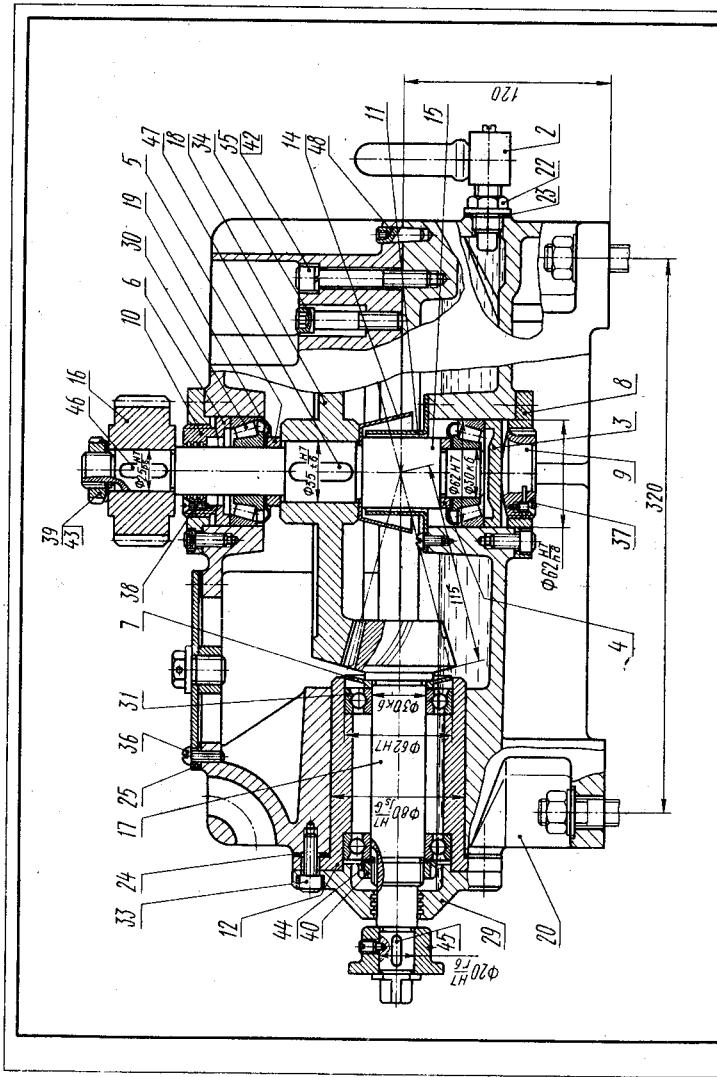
Пример сборочного чертежа конического одноступенчатого редуктора
